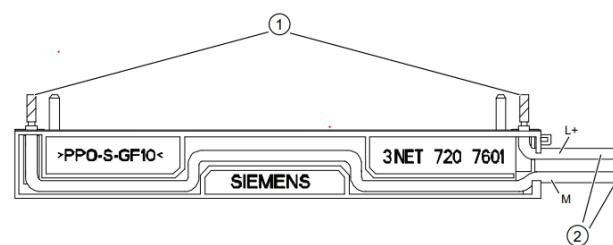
Inserción de los cables de conexión de la tensión de carga en la cámara de cables. Diámetro exterior de los cables >2 mm (vista desde abajo)
